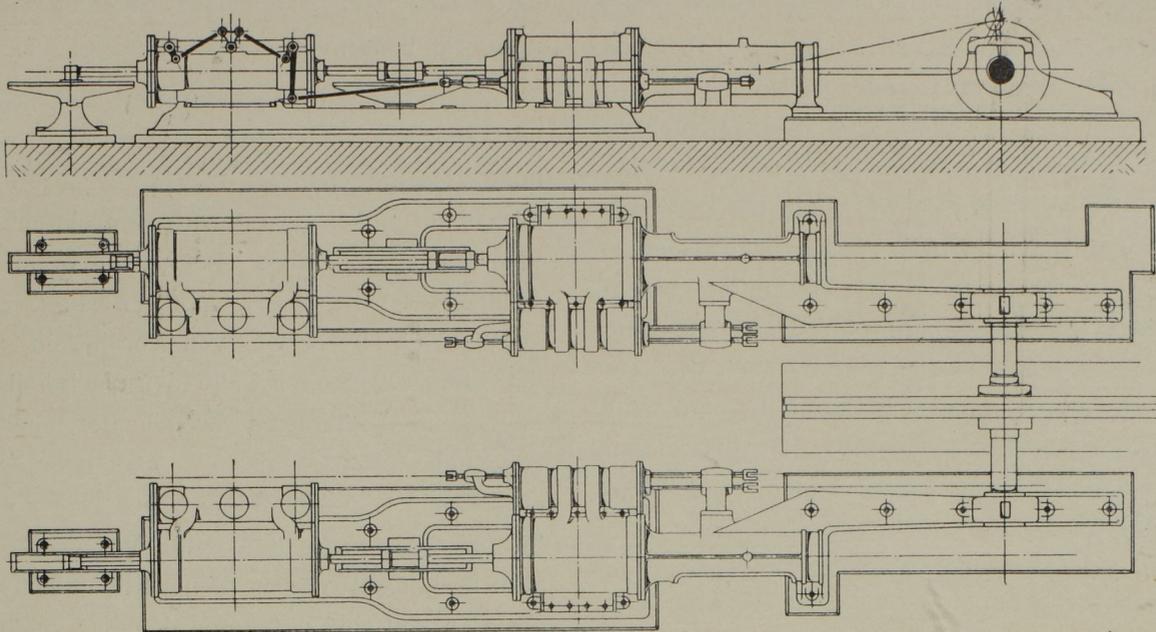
Seitenansicht und Grundriss. Masst. 1 : 80.
